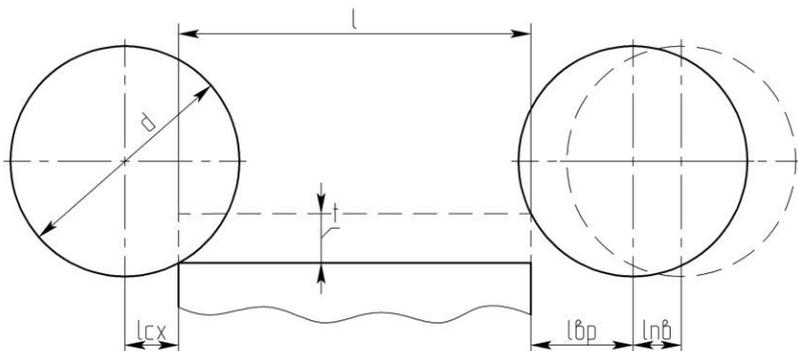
Пример определения расчетной длины обрабатываемой поверхности детали при фрезеровании
